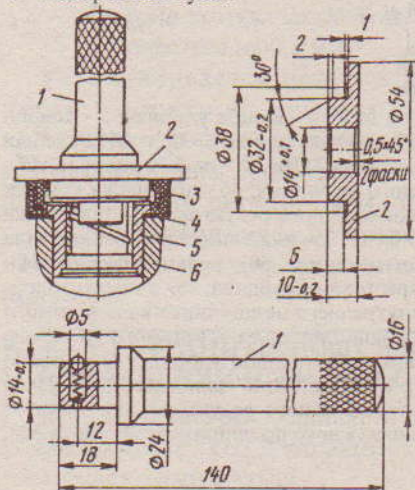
Оправка для выпрессовки наружного подшипника ведомого вала
